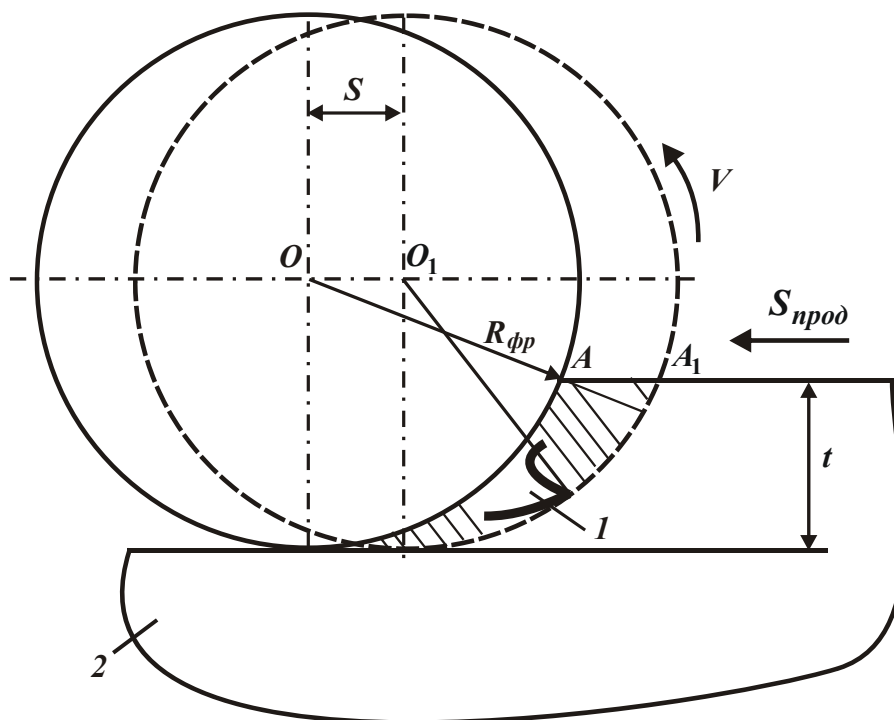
Расчетная схема фрезерования цилиндрической фрезой:
